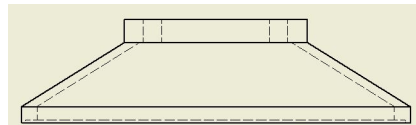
Quinto prototipo de la boya, parte de arriba (vista frontal)
